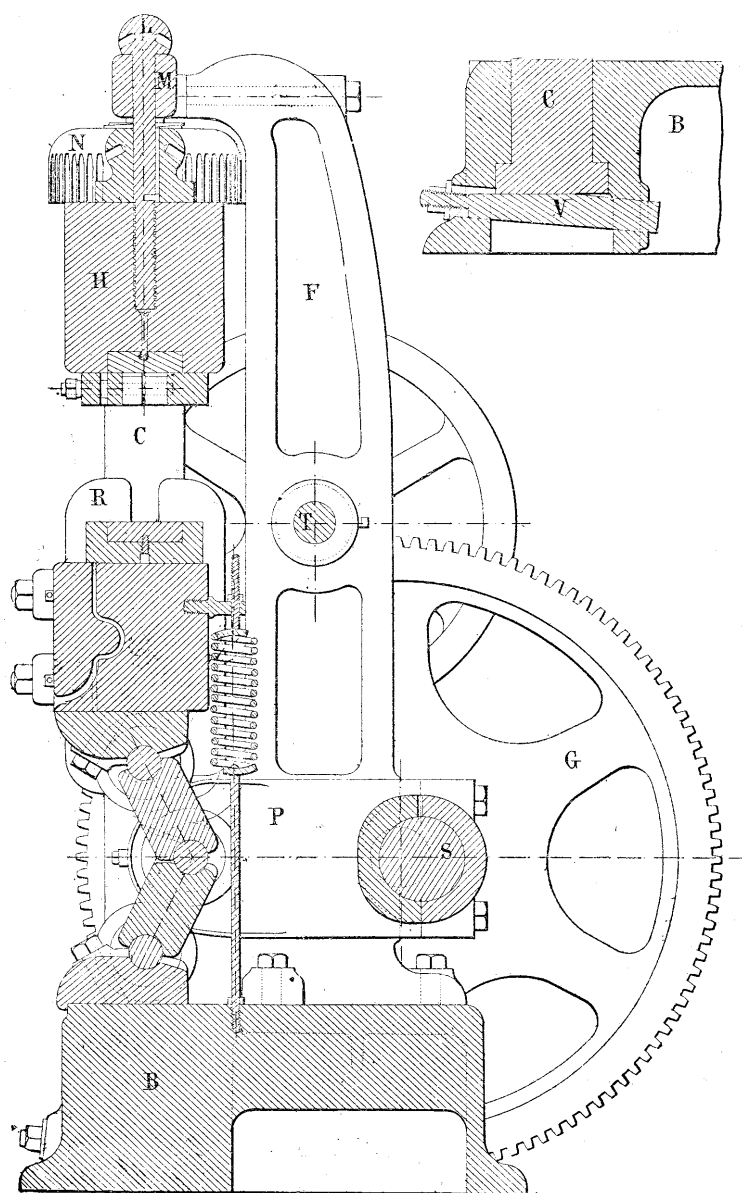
Presse à estamper de la Ferracute Machine Company, de Bridgeton (E.-U.).
